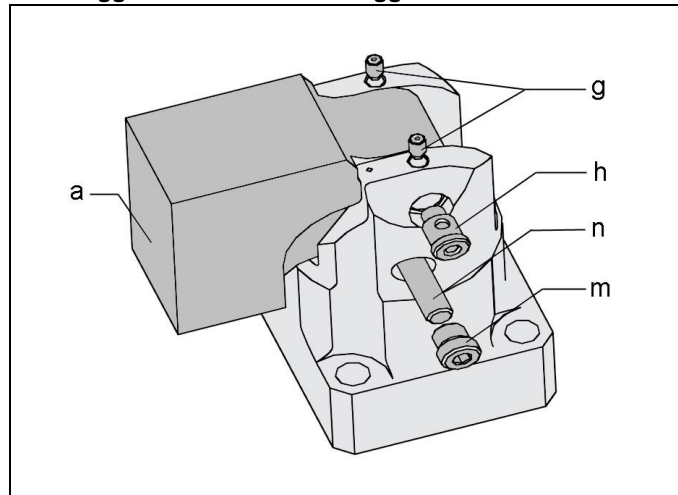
Smontaggio / montaggio della leva di bloccaggio
